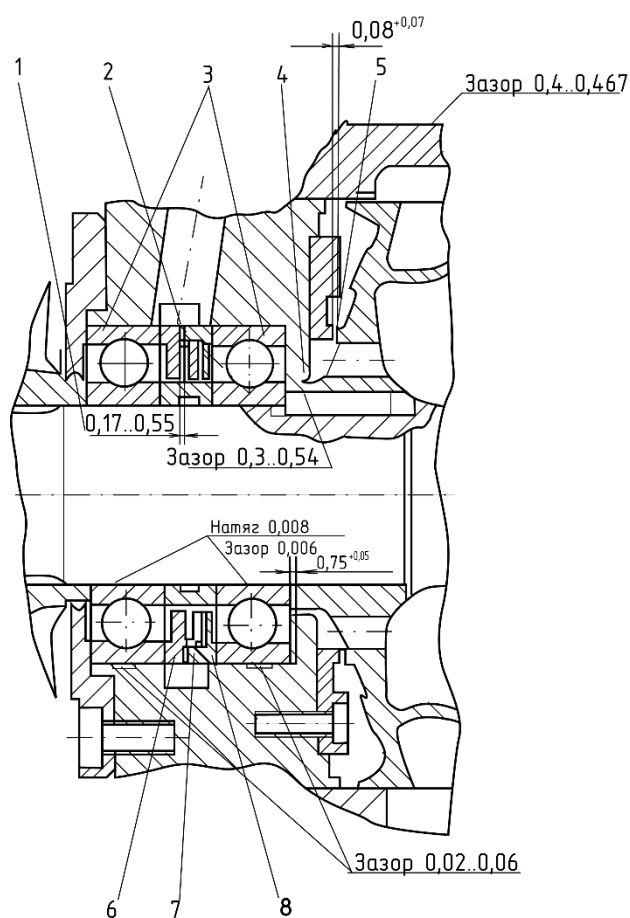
Опора ТНА со сдвоенными шариковыми подшипниками:
